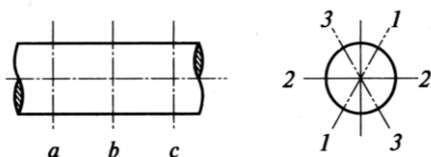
Схема обмера детали цилиндрической формы:
